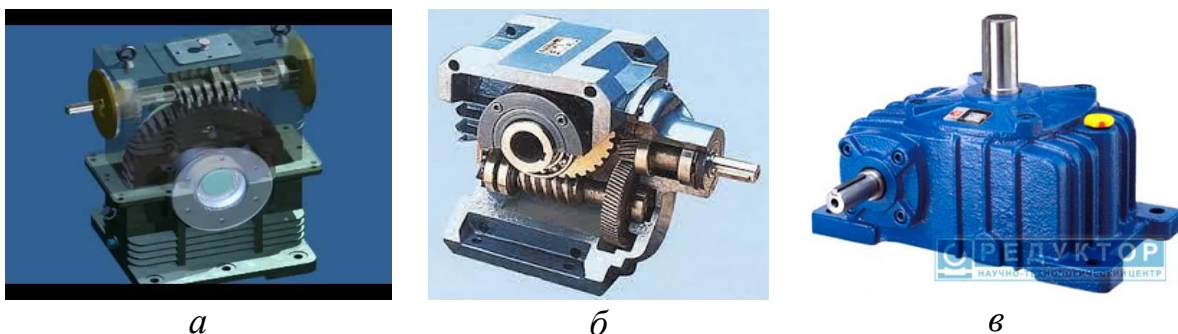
Черв'ячний редуктор: *а* – верхнє; *б* – нижнє; *в* – бокове розташування черв'яка
